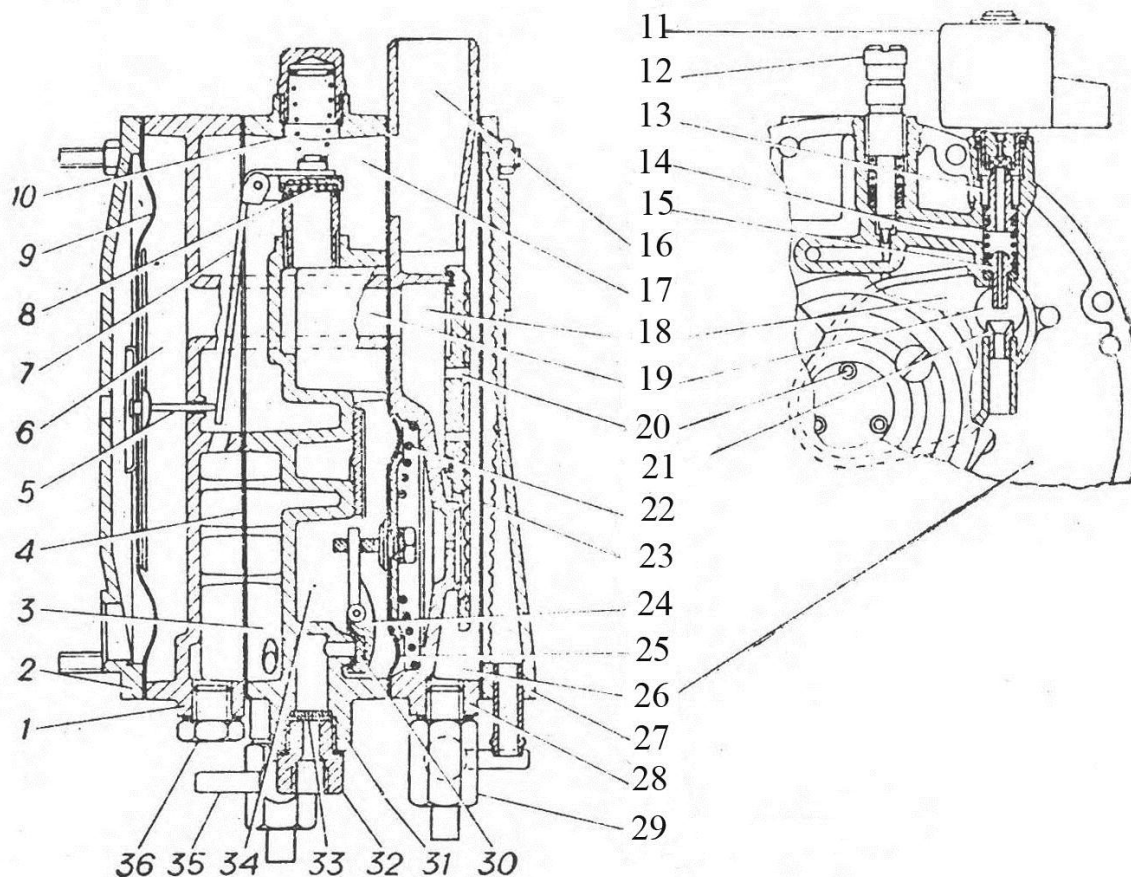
Конструктивные элементы газового редуктора-испарителя
